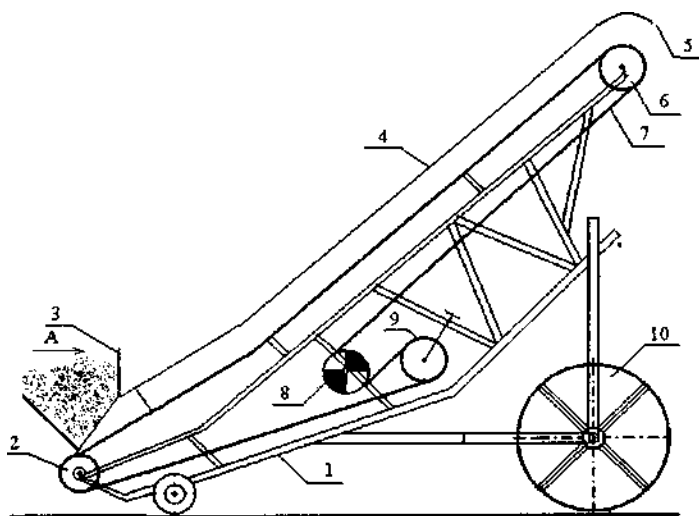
Схема ленточно-трубчатого транспортера: 1 -рама; 2, 6 - ведомые барабаны; 3 - выравнивающее устройство, направляющая труба; 4 - направляющая труба; 5 - оградительный кожух; 7 - транспортерная лента; 8 — ведущий барабан; 9 — натяжной барабан; 10 — опорные колеса
